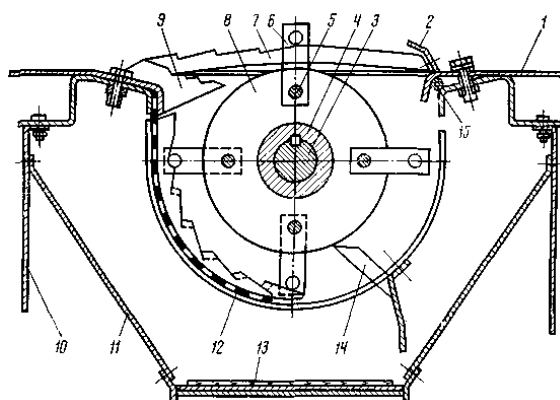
Устройство ротора дробилки-измельчителя ИРТ-165 для измельчения соломы повышенной влажности: 1 - днище; 2 - отсекатель; 3 - вал; 4 - кольцо; 5 - ось; 6 - молоток; 7 - лифтер; 8 - диск; 9 - гребенка; 10 - рама; 11 - боковина; 12 - дека; 13 - горизонтальный транспортер; 14 - отражатель деки; 15 - труба
